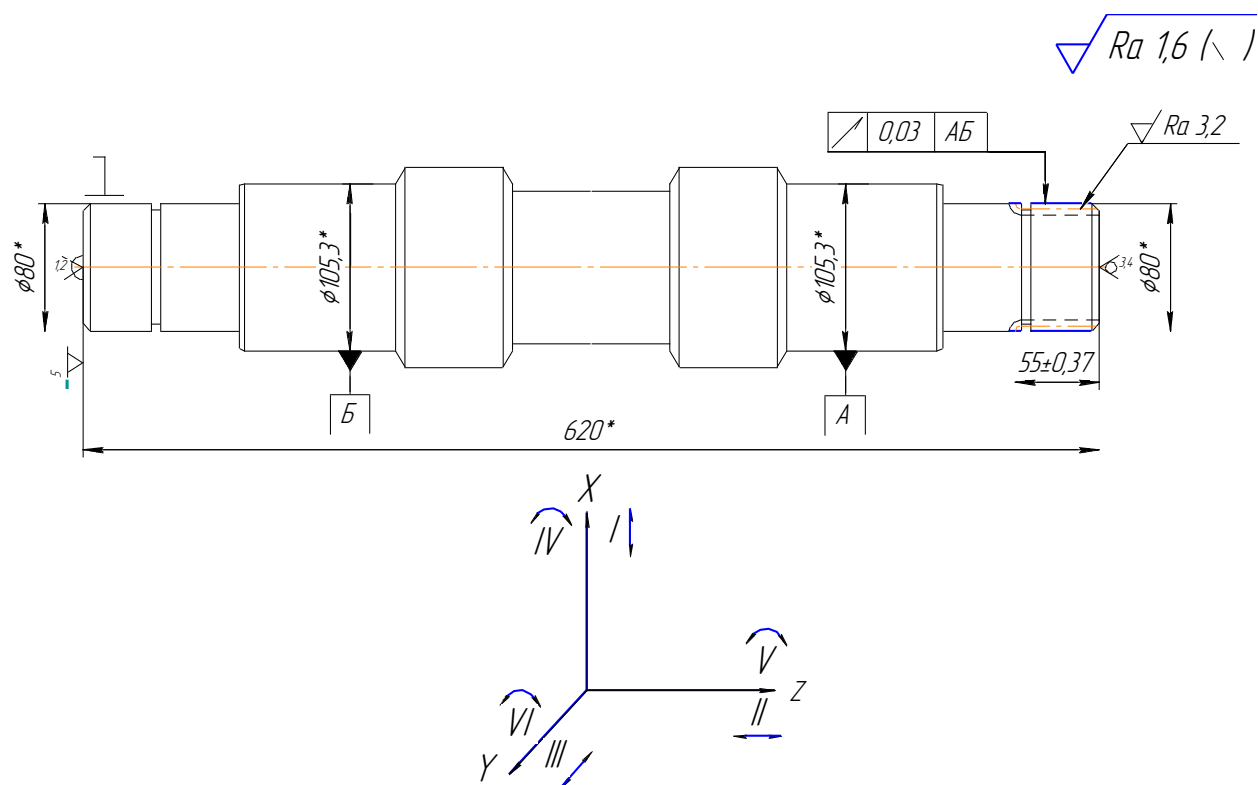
Схема базування Вала-шестерні на зубофрезерній операції 070
